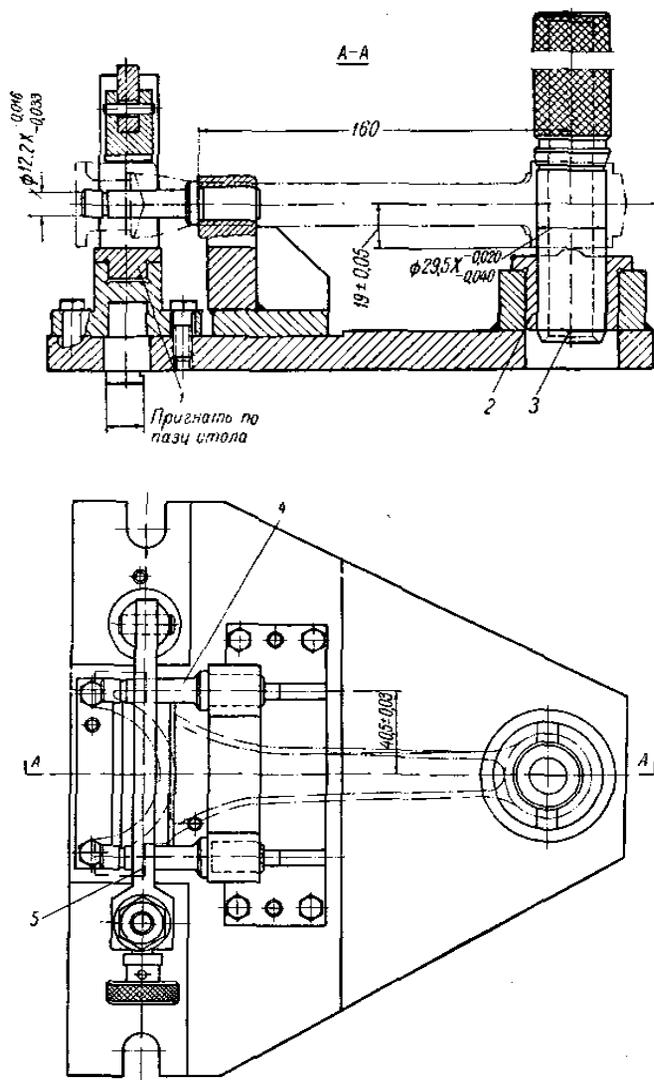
Приспособление для фрезерования торцов разъема нижней головки шатуна
